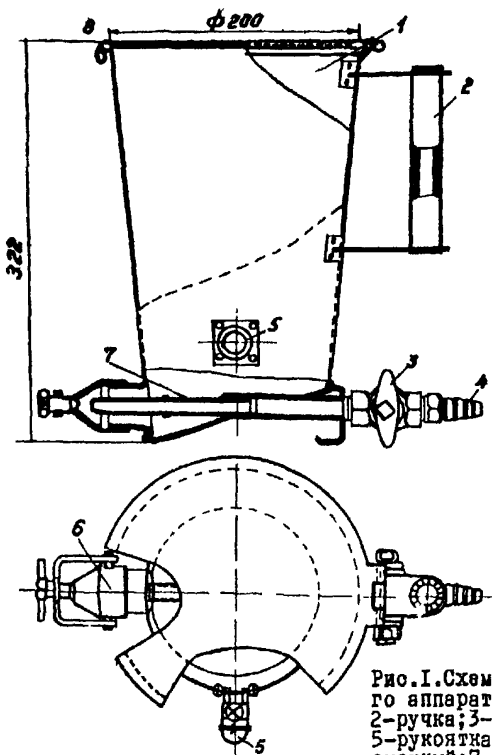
Схема распылительного аппарата: 1-корпус; 2-ручка; 3-маховик; 4-нипель; 5-рукоятка; 6-наконечник сменный; 7-трубка; 8-крышка.
